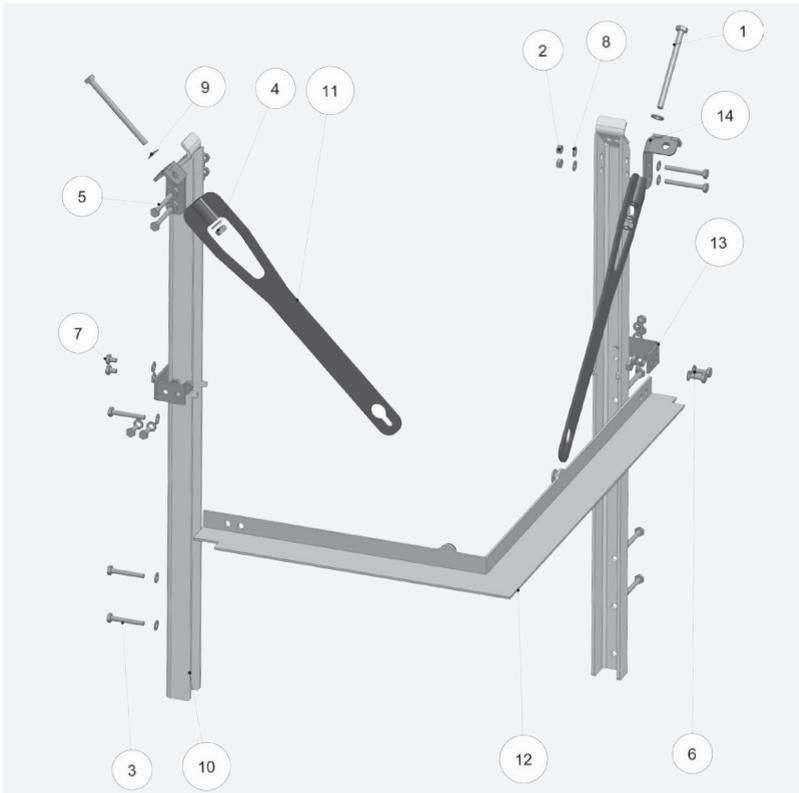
Zubehör Tragrahmen für den FINA go ES, Explosionszeichnung
